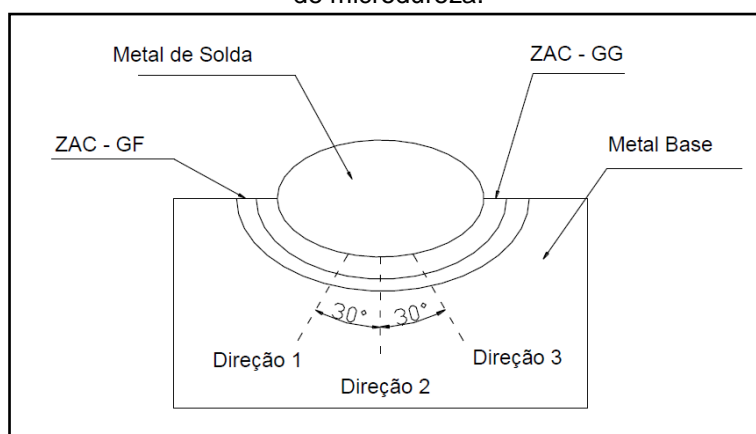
Amostra soldada para avaliação do envelhecimento.
